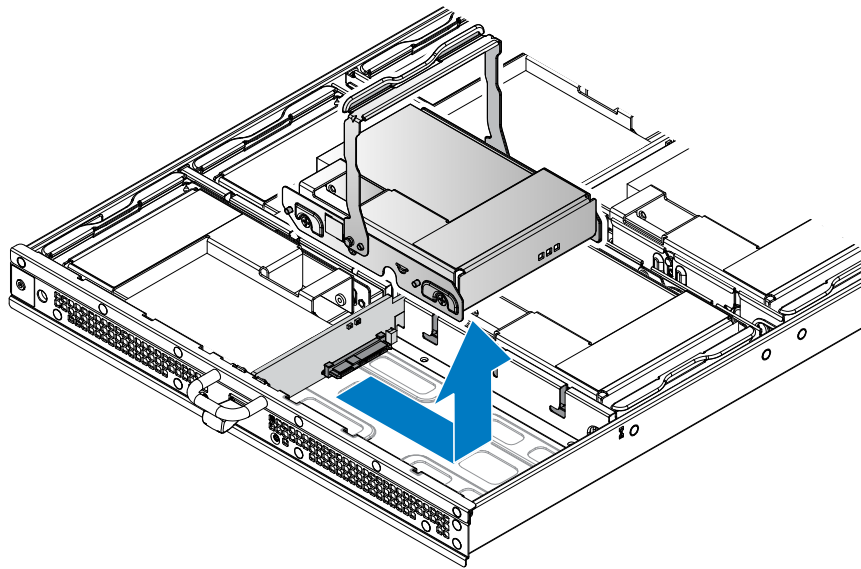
Entfernen der 2,5-Zoll-Festplattenbaugruppe
